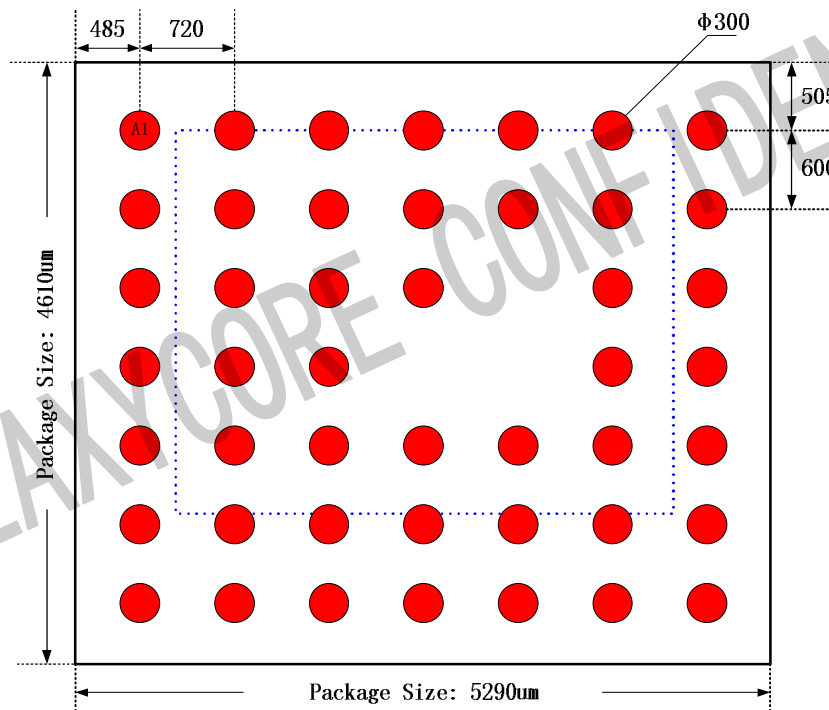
PCB 焊盘设计说明示意图(Top View)
